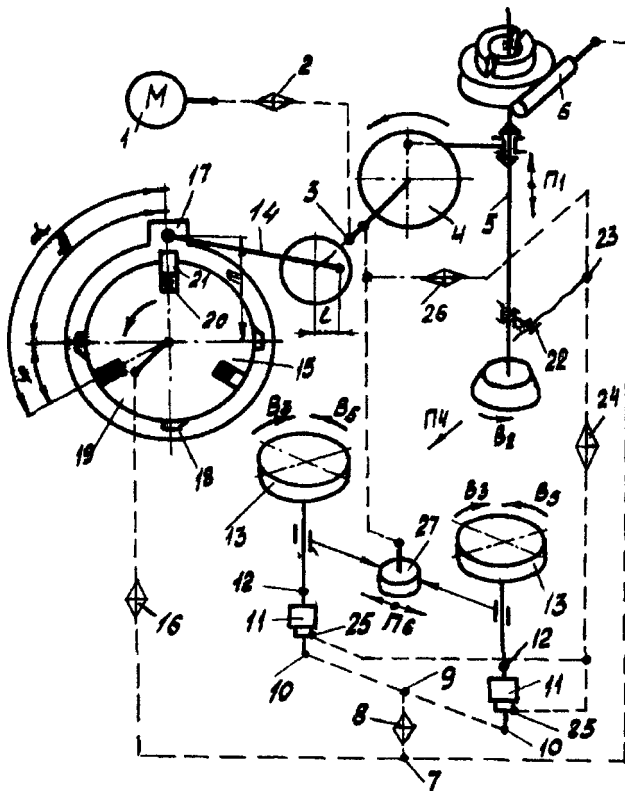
Кинематико-компоновочная схема станка для параллельной обработки двух зубчатых колес
